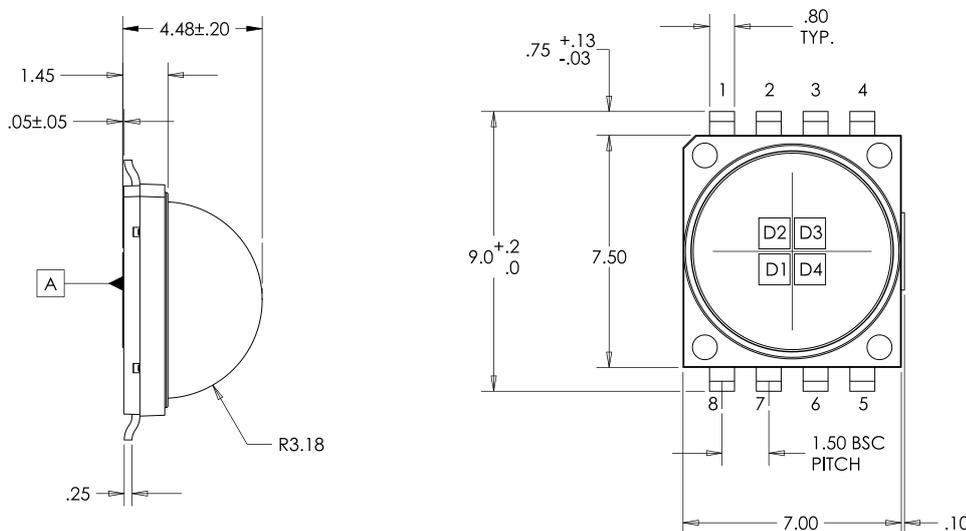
Габаритный чертеж корпуса светодиода серии MC-E
